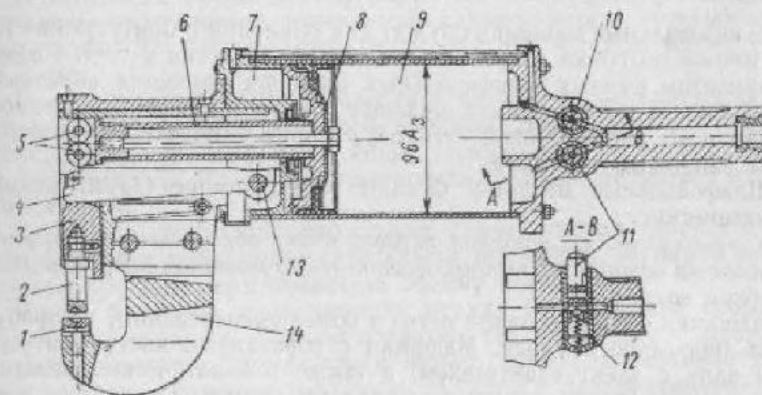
Пневматический рычажный пресс ПРП5-2.
